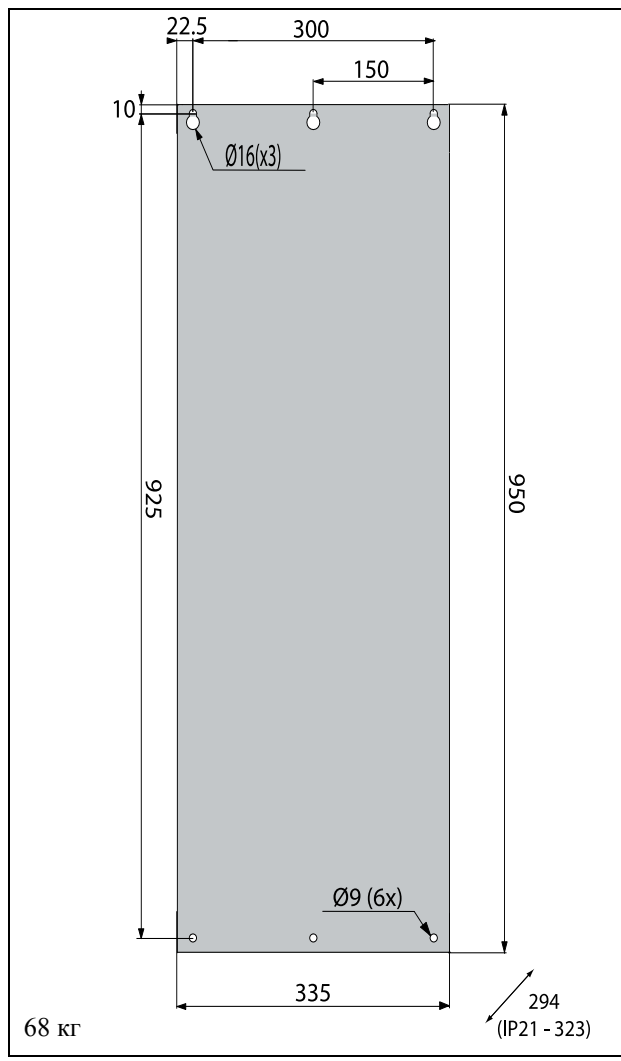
Устройство Etotron /FDU моделей 48-205 – 48-244 (типоразмер корпуса F2).
